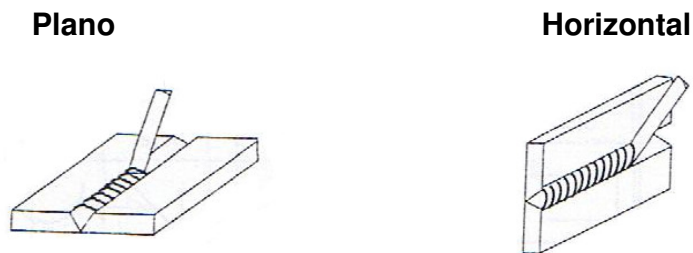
Posiciones de soldadura del S.A.S
